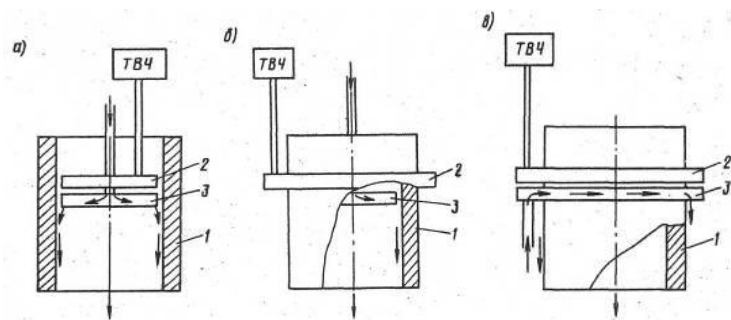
Схема обробки деталей струмами високої частоти:
